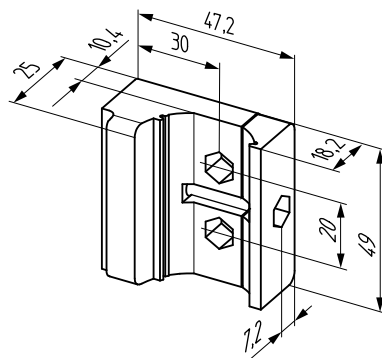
Габаритный чертеж держателя QuickFix (2066048)
